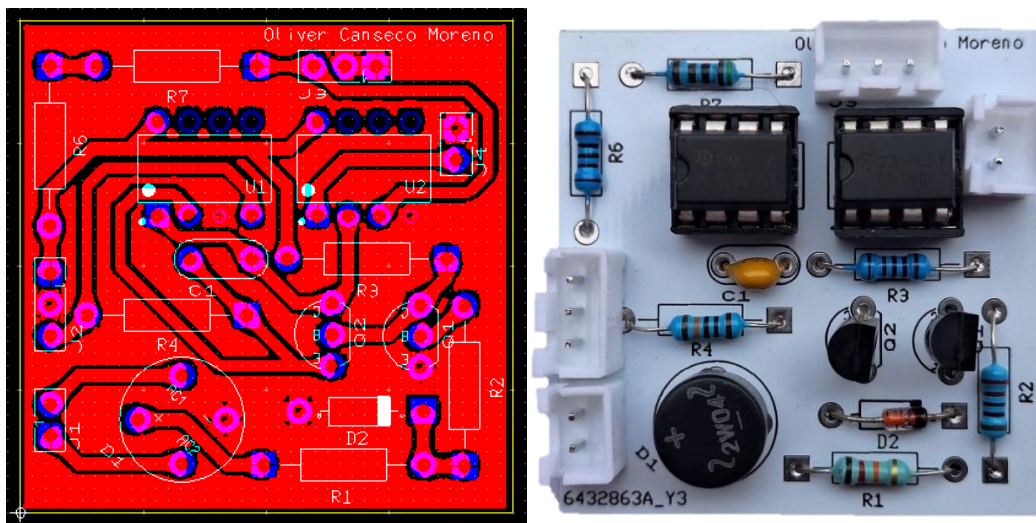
Diseño y manufacturación del PCB para el generador PWM sincronizado a la red eléctrica
